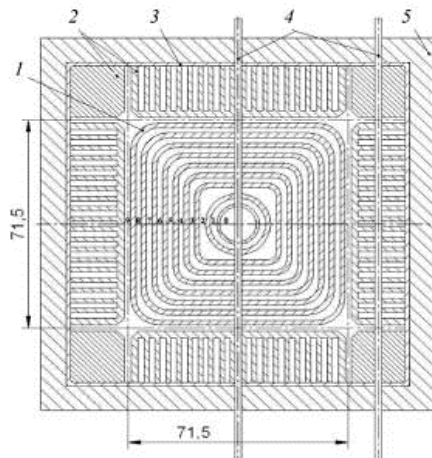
Поперечный разрез колонки гидравлического стенда [1]:
